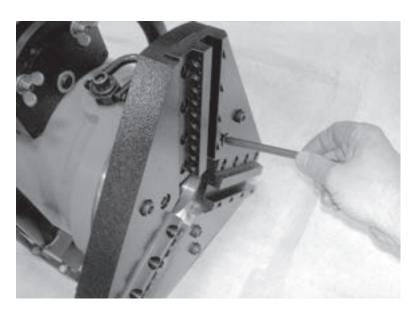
Entfernen Sie die Auslöserbaugruppe.
